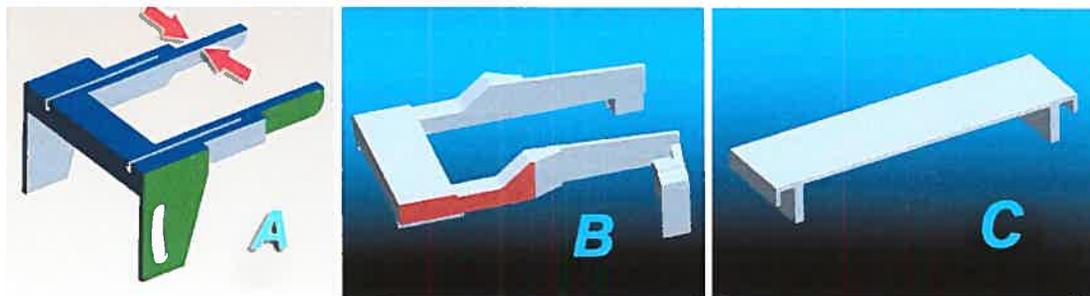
Dessin des pièces du Sixième modèle 3D, option B.¹⁷⁴
